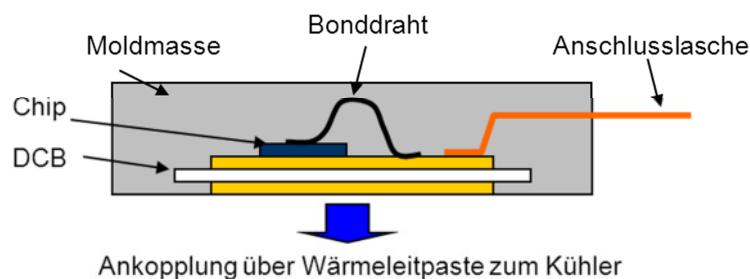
Aufbautechnik Moldmodul (Prinzipskizze)
